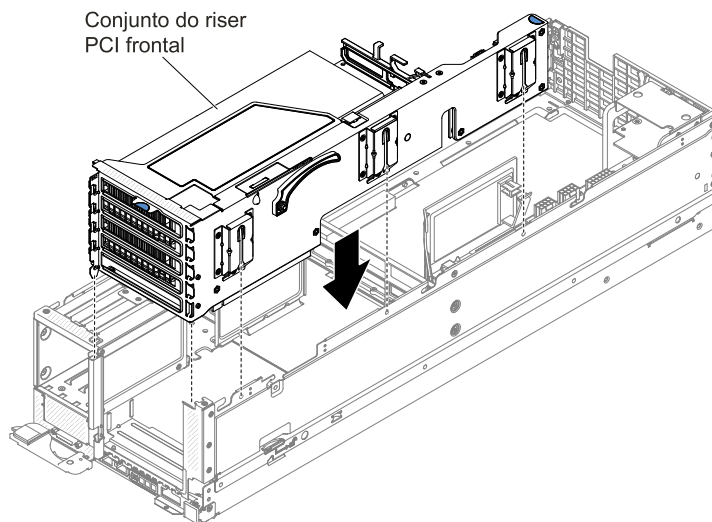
Instalação do conjunto do compartimento da placa riser PCI frontal
